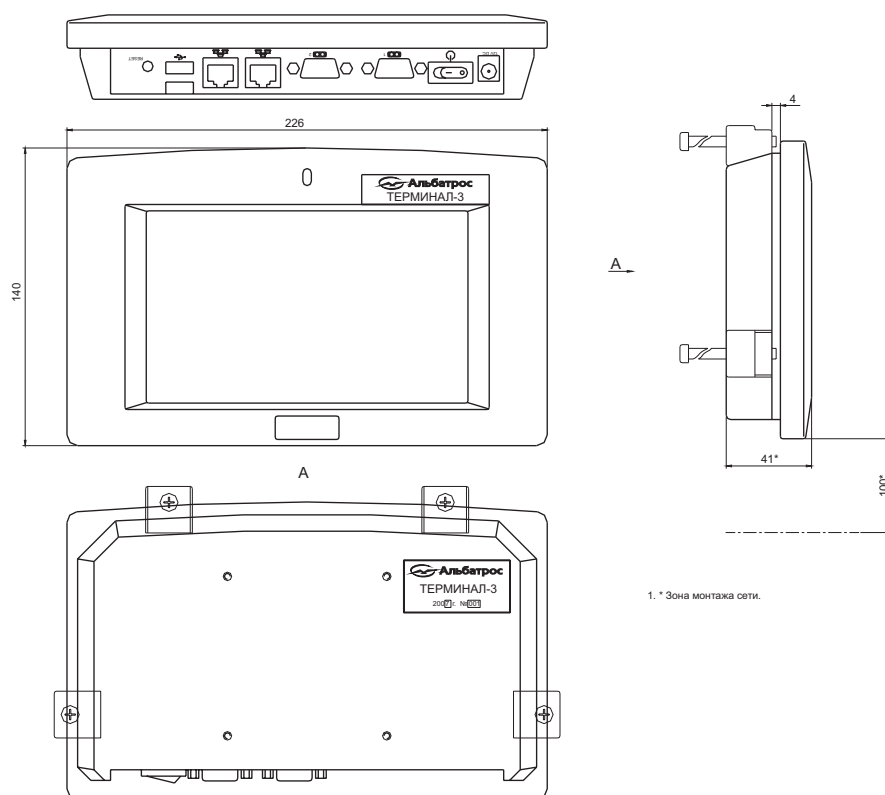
Внешний вид и габаритные размеры Терминала-3
